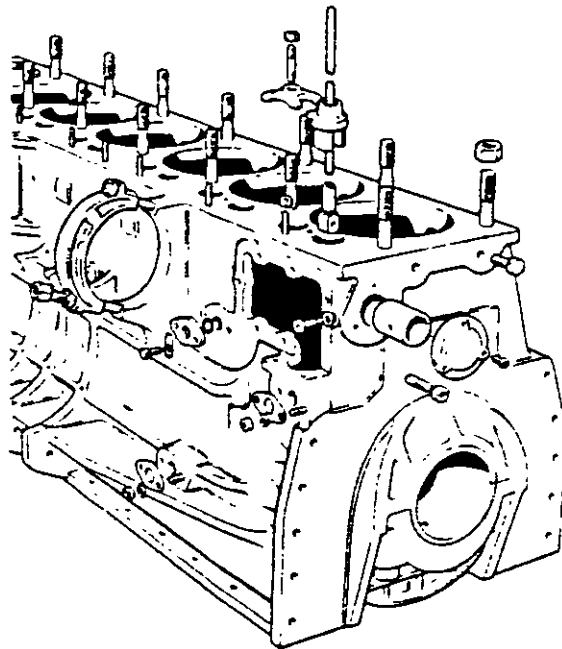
3 Monoblock de un motor de 6 cilindros en línea
